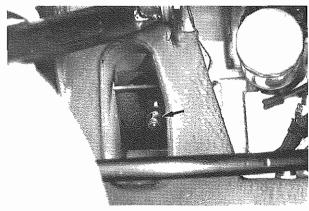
Viti di fissaggio laterale motore - Side engine screws
